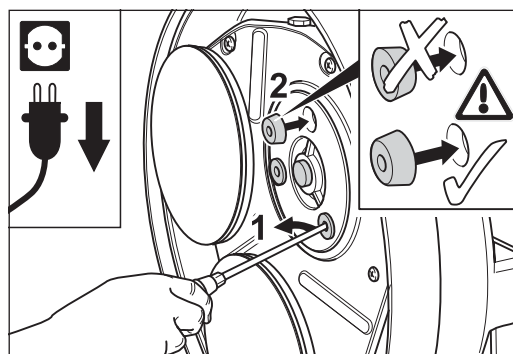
Die Gummilager mit einem Schraubendreher aus der Tellerriemenscheibe hebeln (1).
